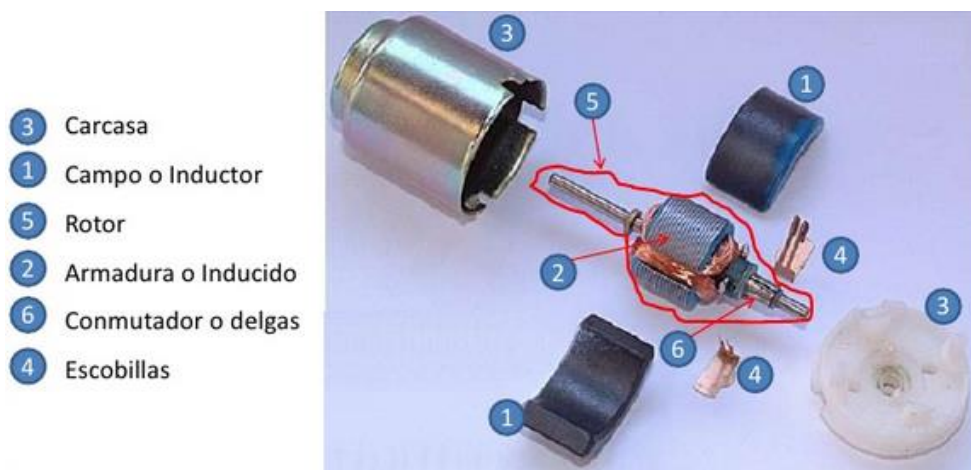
Despiece motor brushed, ("Sesión 6 motor dc," 18:40:14 UTC)
